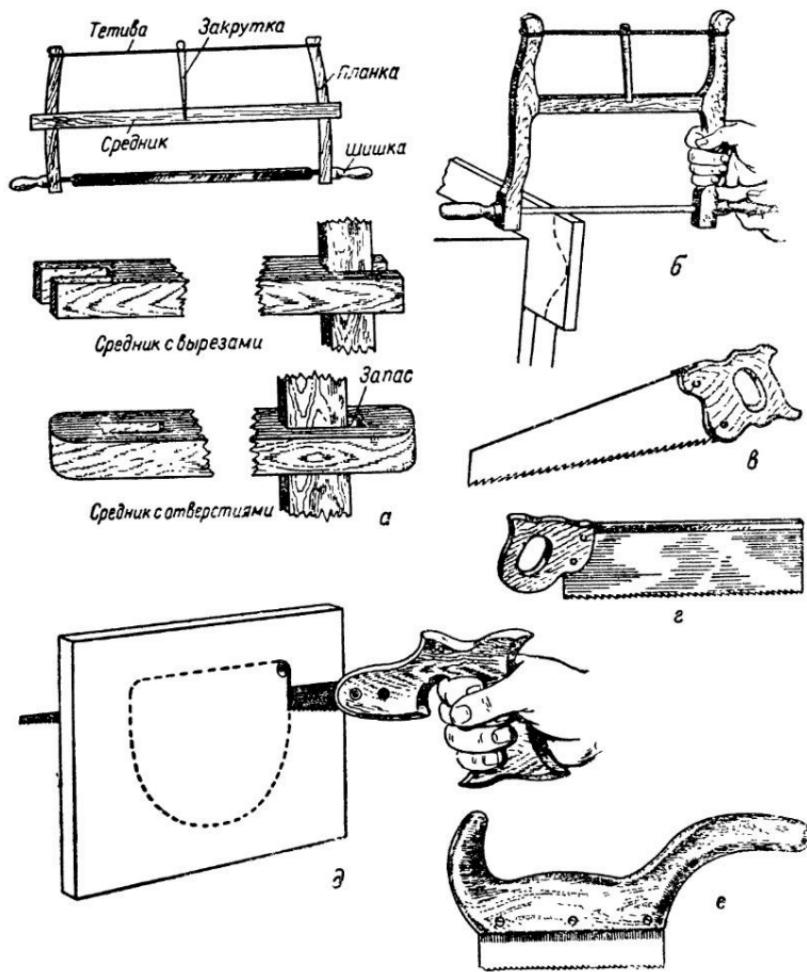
Пилы: а — лучковая пила и ее части; б — выкружная лучковая пила; в — широкая ножовка; г — ножовка с обушком; д — узкая ножовка; е — наградочная ножовка.
